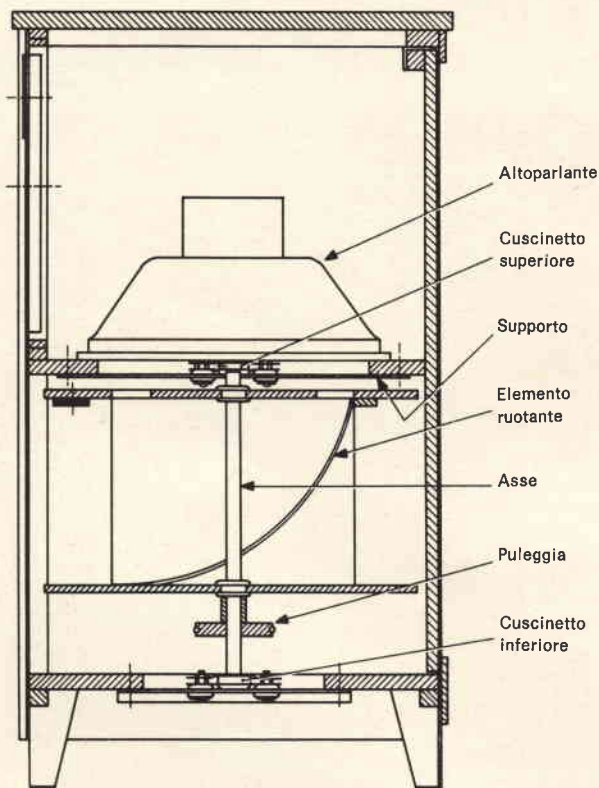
Piano di montaggio dell'altoparlante e dei vari meccanismi che compongono il tremolo «Leslie».
